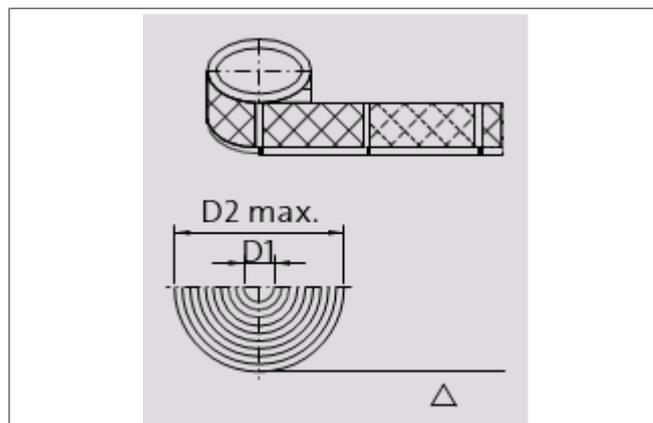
Sens d'enroulement des bobines pour sens de marche de la machine de droite à gauche
